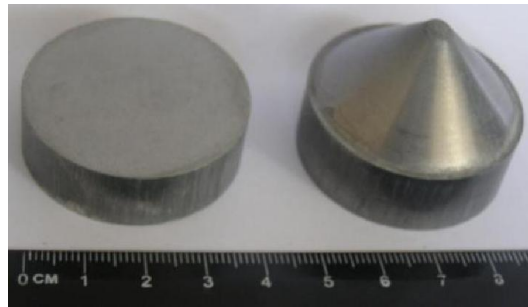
Зовнішній вигляд заготовок для гарячого штампування
